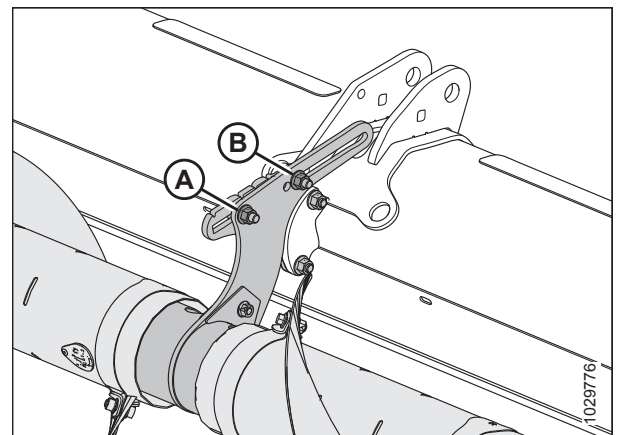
Posición inicial de los montajes ajustables: sinfín de dos piezas
